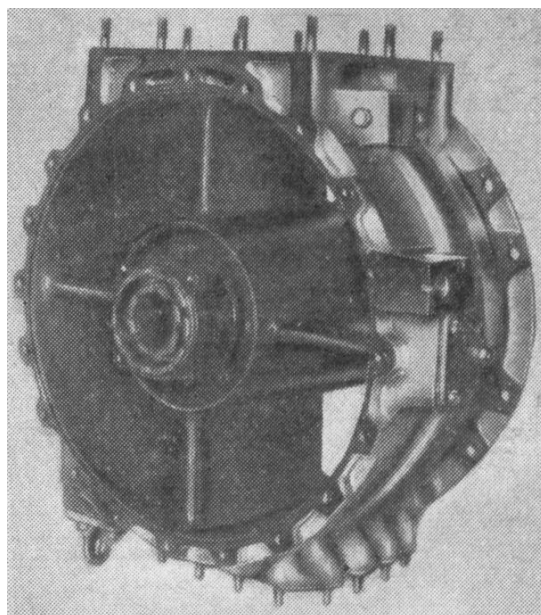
Первая опора роторов двигателя (вид сзади слева)
